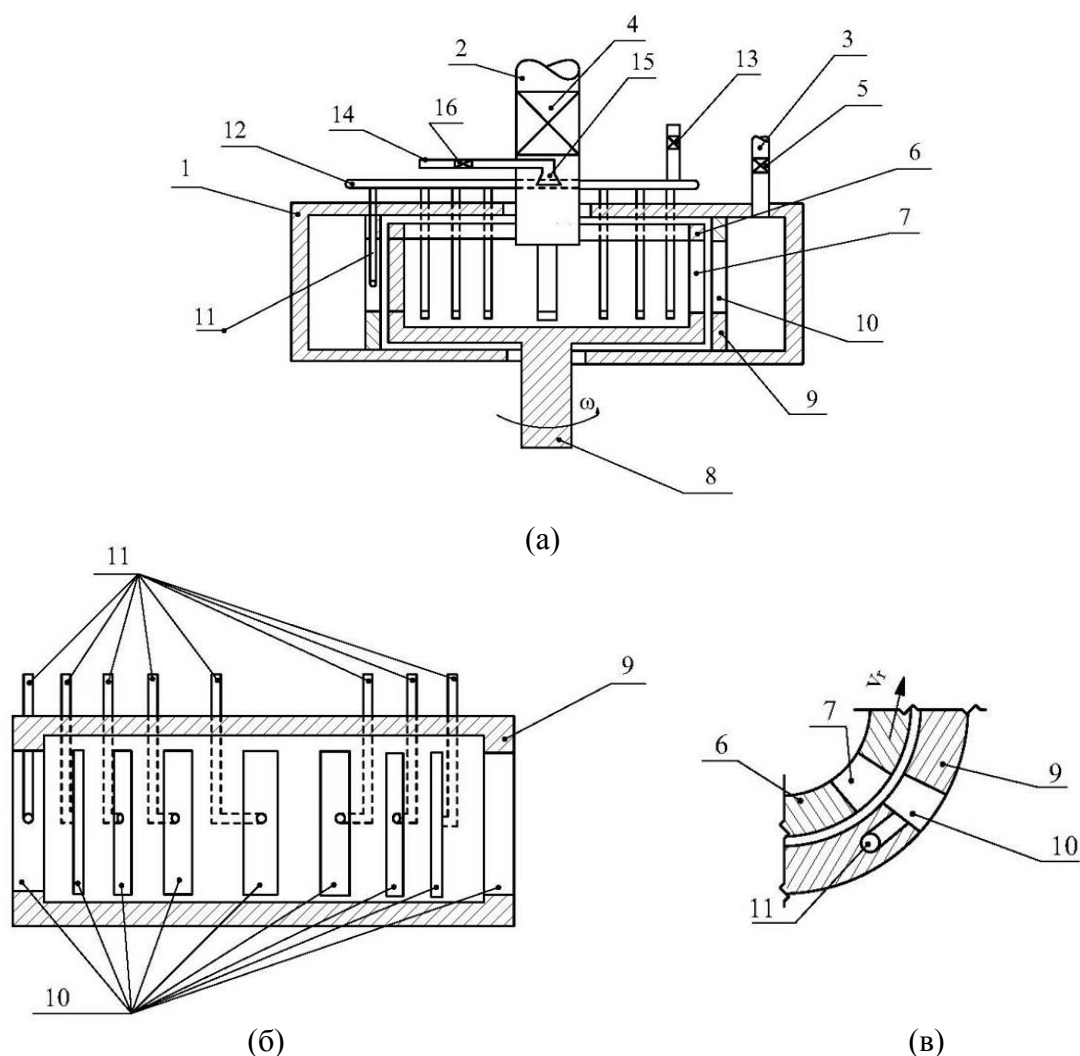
Роторный аппарат типа ДМП для приготовления рабочей жидкости: диспергатор с модуляцией потока (а); статор с дополнительными каналами для подачи или отсоса воздуха (б); модулятор (в)
